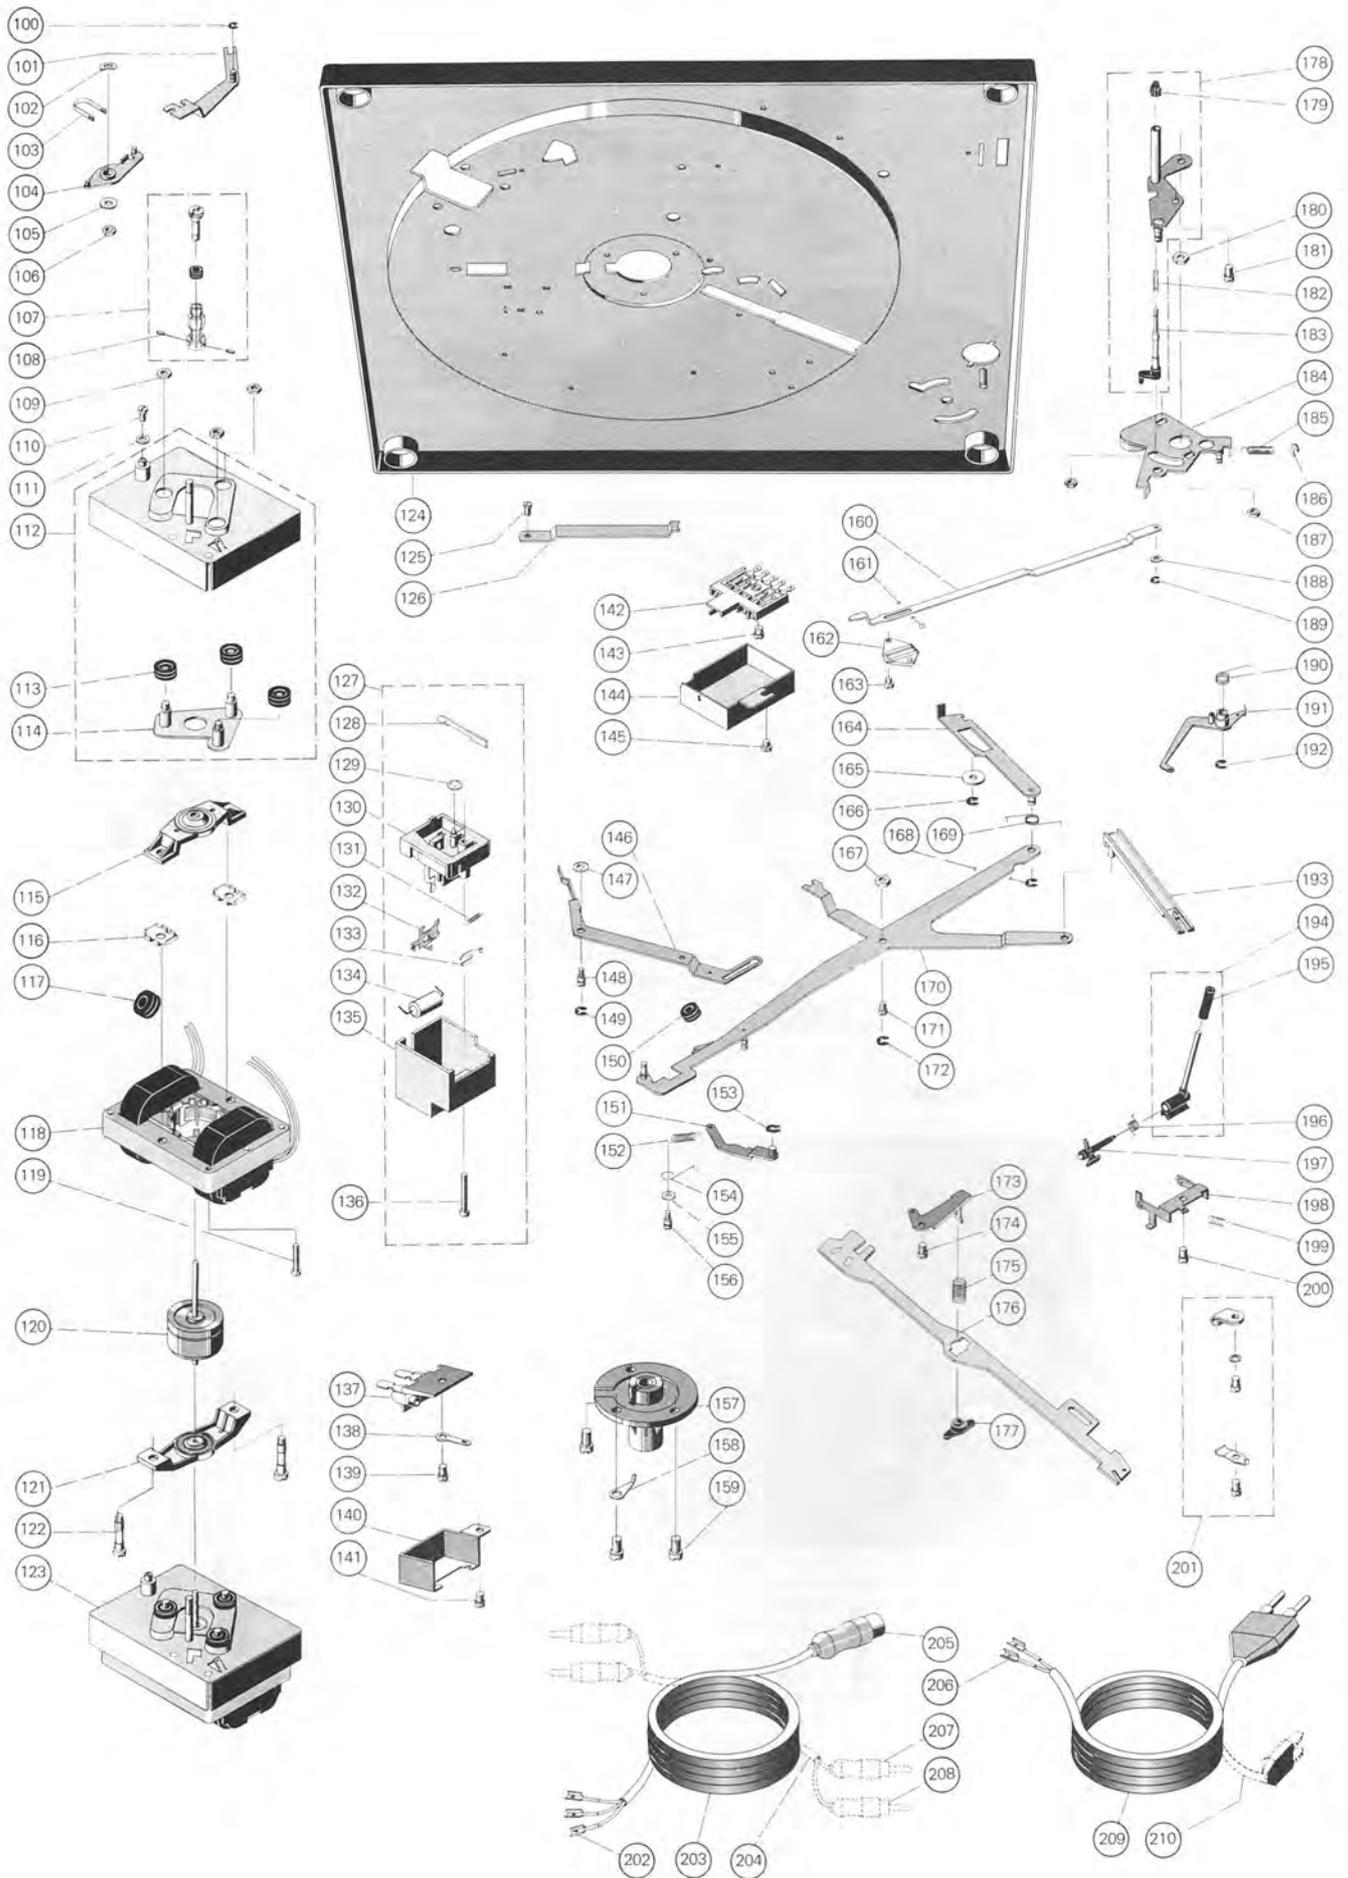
Explosionszeichnung Teile unter der Einbauplatte
